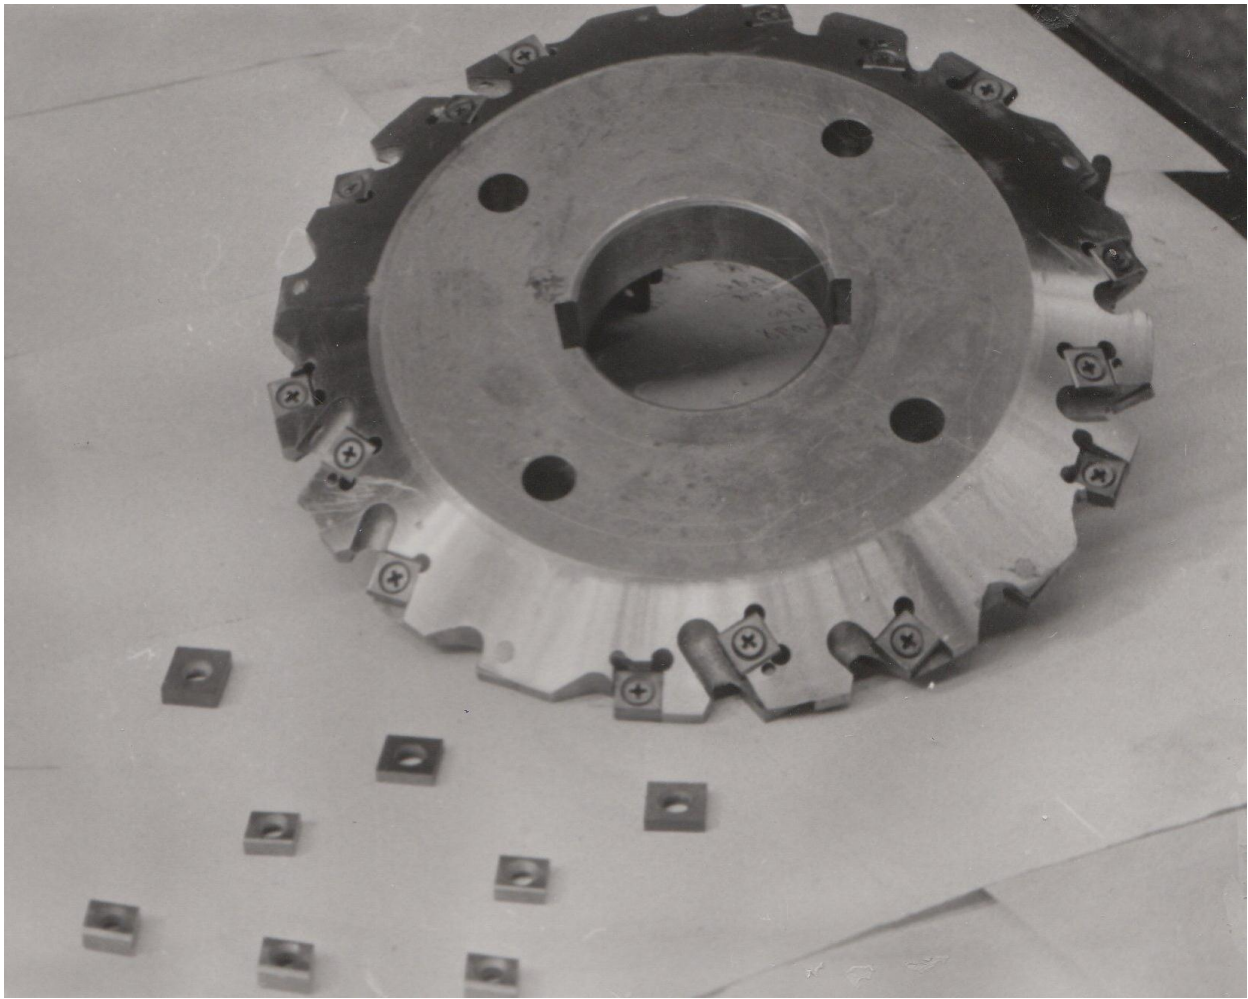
Дисковая зуборезная фреза с механическим креплением пластинок
